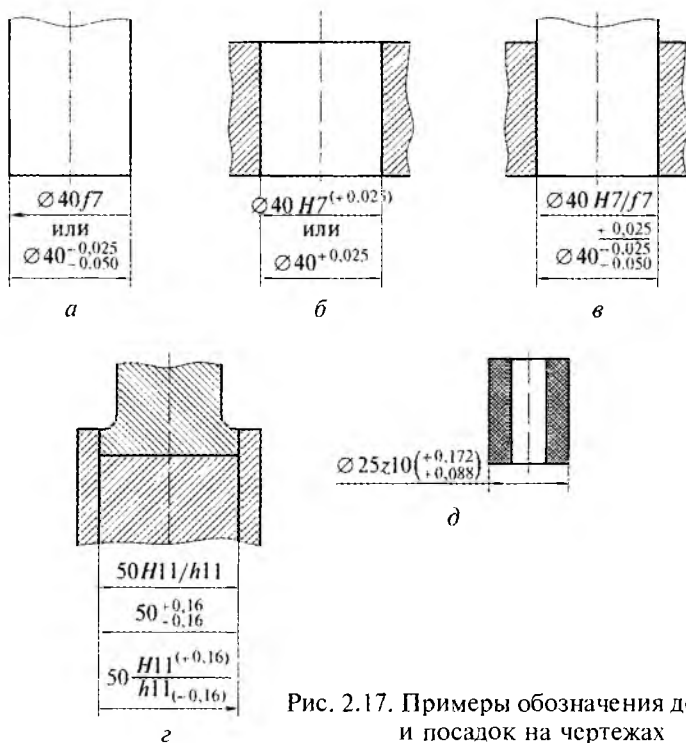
Примеры обозначения допусков и посадок на чертежах
